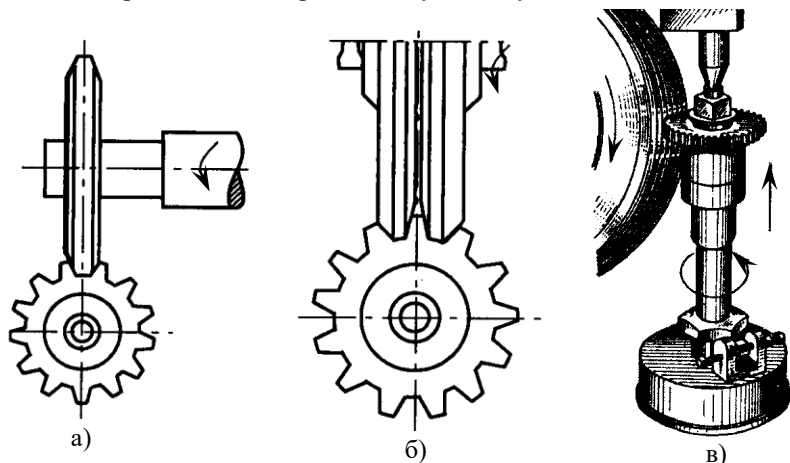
Шліфування зубів циліндричних зубчастих коліс:
